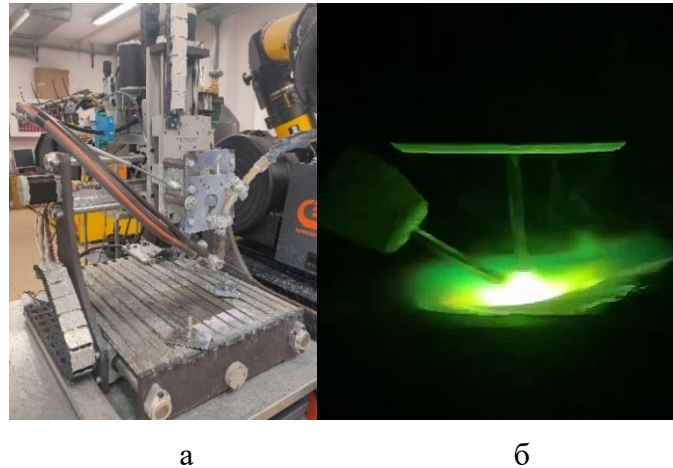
Установка для исследования процессов наплавки и аддитивных технологий: а – общий вид установки б- процесс наплавки.
